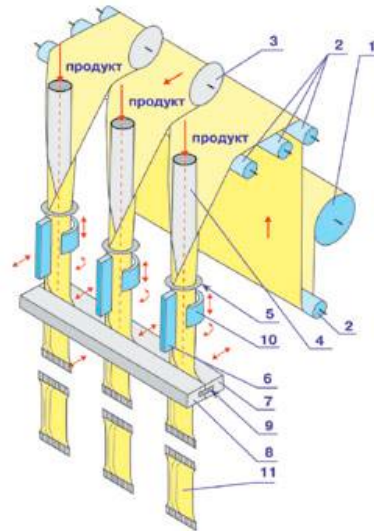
Багатопотокове компонування машини: 1 – плівка; 2 – направляючі валки; 3 – механізм розрізання плівки на смуги; 4 – рукавоутворювач; 5 – фіксатори; 6 – губки поздовжнього зварювання; 7, 8 – губки поперечного зварювання; 9 – відрізний ніж; 10 – механізм протягування; 11 – готовий пакет
